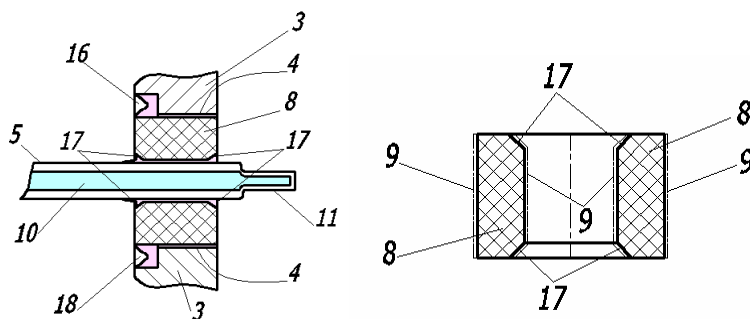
Керамический изолятор металлокерамического корпуса типа КТ–97С
